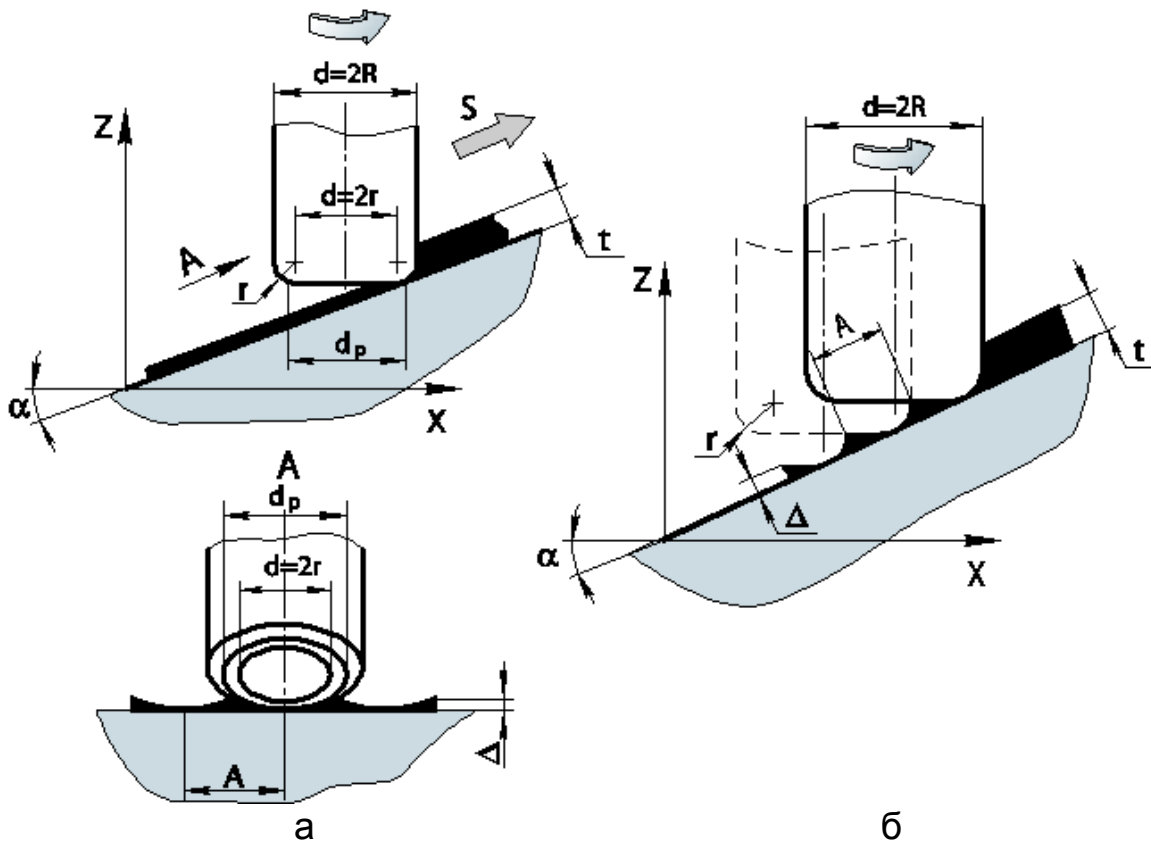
Схеми трикоординатного фрезерування вздовж (а) і поперек (б) похилої ділянки поверхні заготовки
